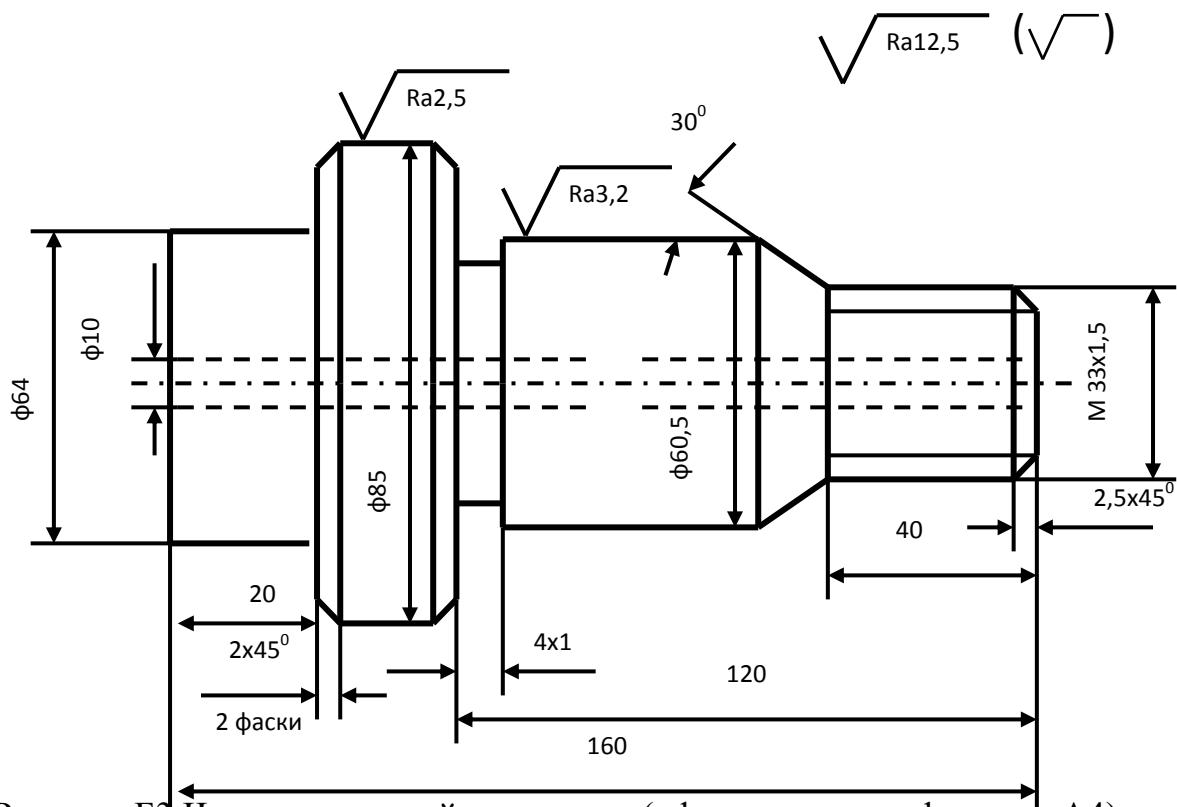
Чертеж токарной заготовки (оформляется на формате А4)
